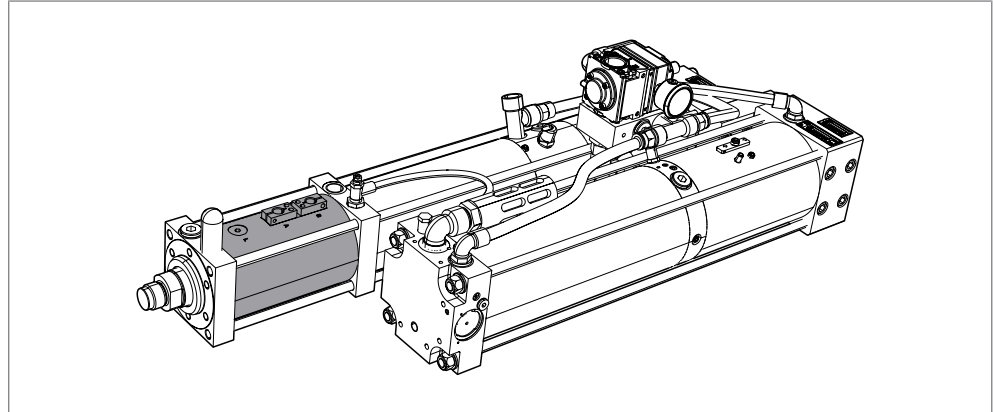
Prehľad výrobkov Kraftpaket s tlmením nárazu pri reze ZSD
